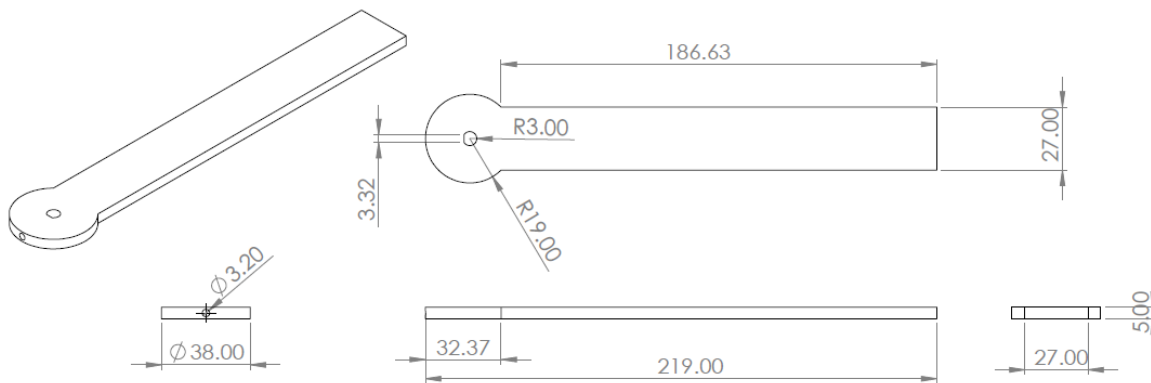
Dimensiones de pieza móvil que se encuentra vinculada al eje del encoder incremental.
